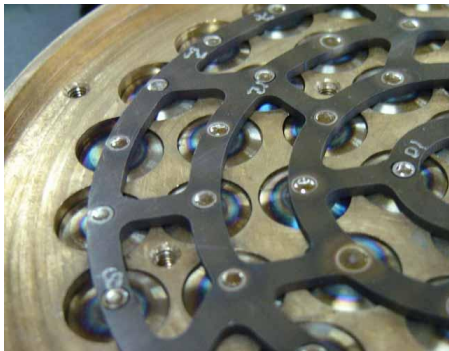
1^{er} prototipo de soldadura de grilla CARA.
